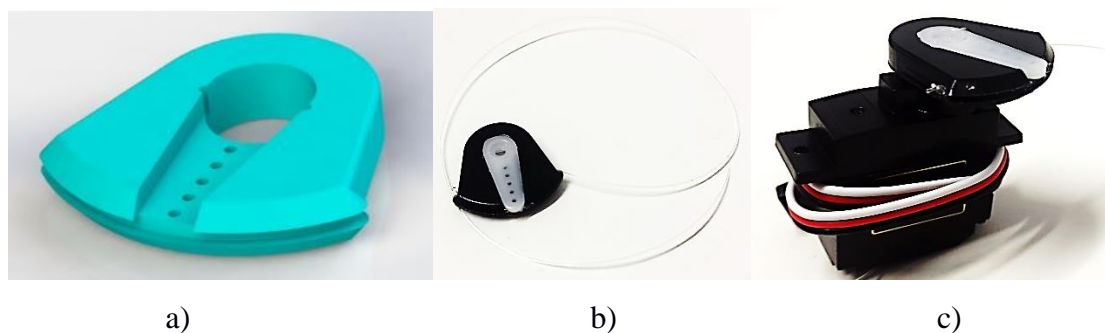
Acople: a) Diseño CAE. b) Modelo 3D-impreso. c) Montaje en el servo.
